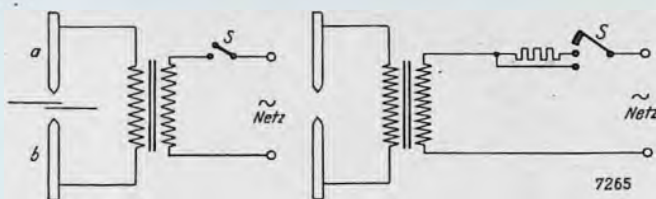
Schema der Punktschweißung (links) und Schaltung des beschriebenen Schweißgerätes (rechts)
